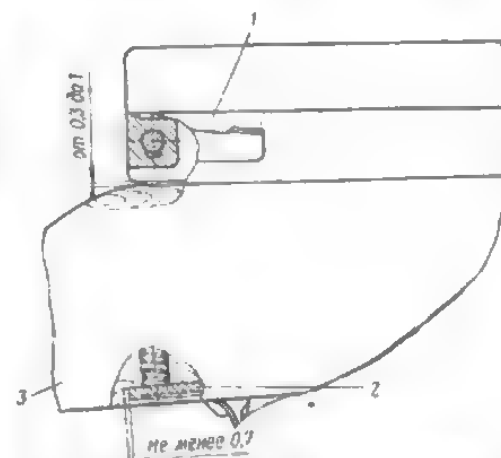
Сборка ложи со ствольной коробкой и ударно-спусковым механизмом:
